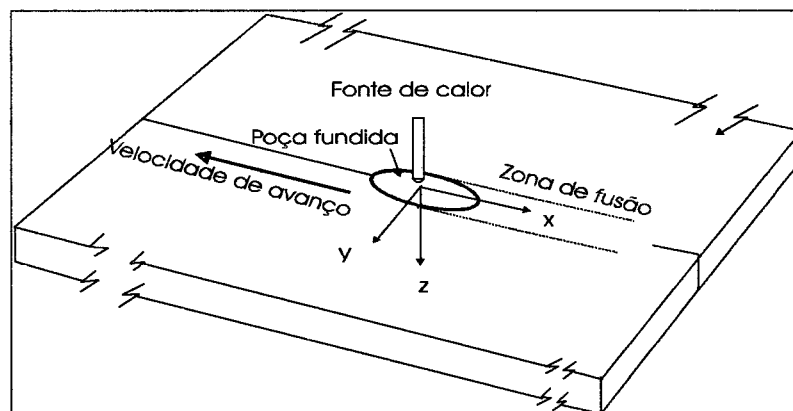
Esquema de um cordão sobre a superfície de uma chapa infinita para condições de fluxo de calor tridimensional [15].
